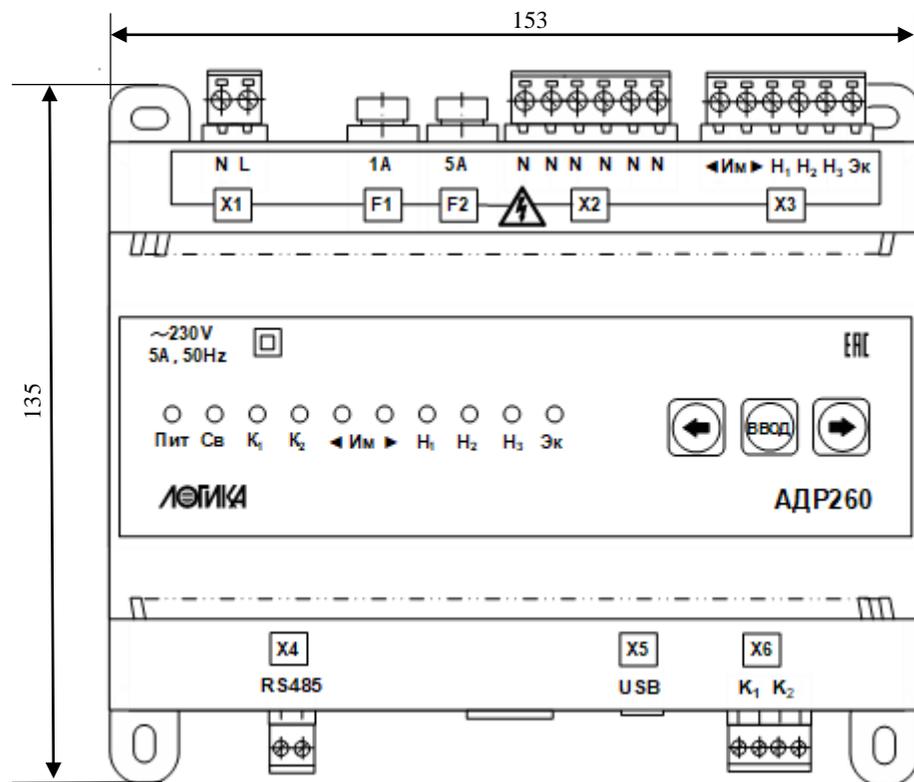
Адаптер АДР260, вид спереди, габаритные размеры.
